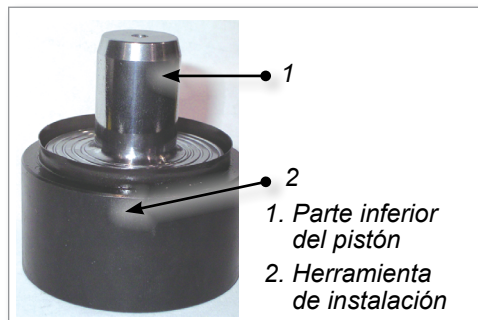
Parte inferior del pistón con herramienta de instalación
